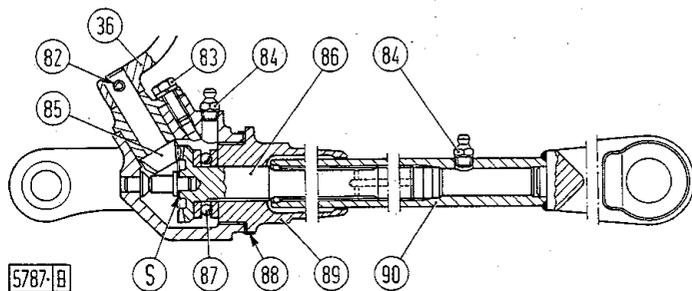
Sezione sull'albero di sollevamento bracci.
